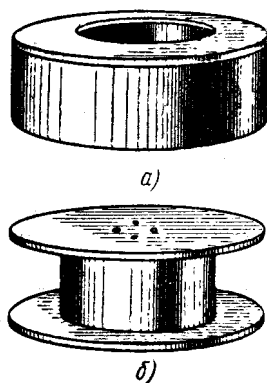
Кассеты для сварочной проволоки:
